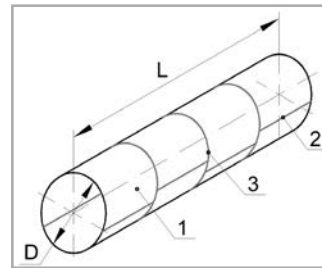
Схема сварной обечайки котла железнодорожной вагоноцистерны, сваренной из царг (коротких обечаек): 1 — царга; 2 — продольный сварной шов царги; 3 — кольцевой сварной шов обечайки; D — внутренний диаметр обечайки; L — длина обечайки
